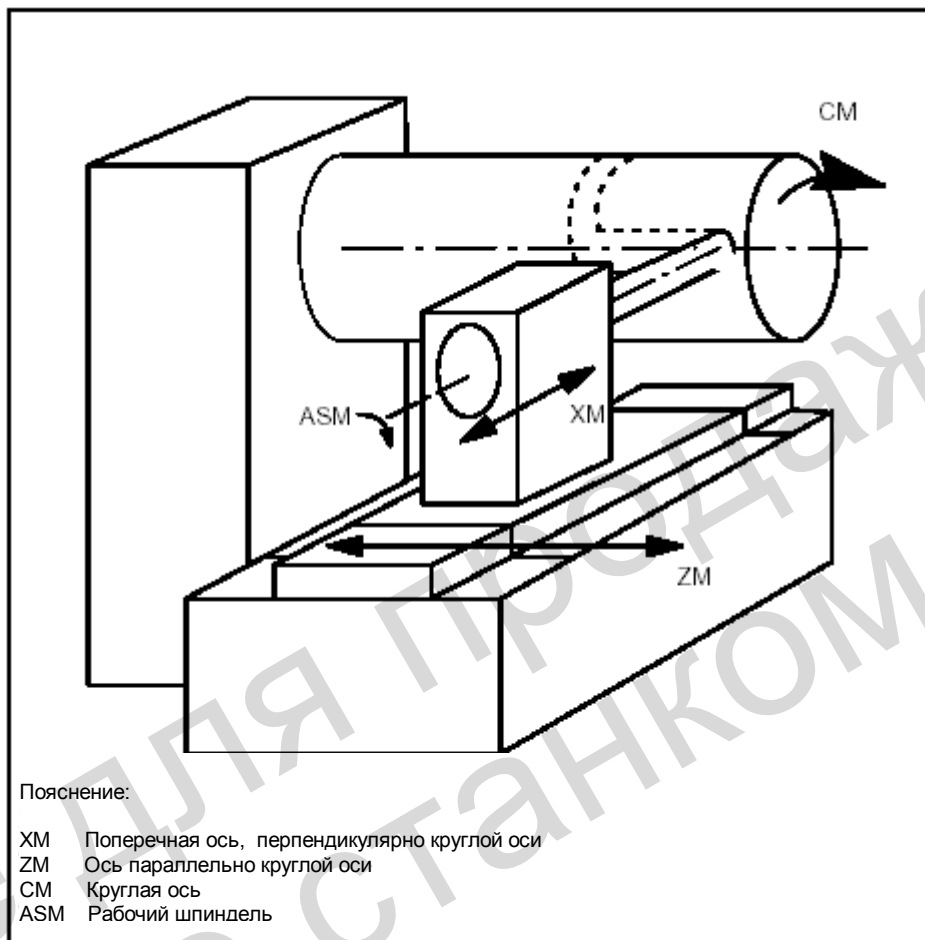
Обработка паза на боковой поверхности цилиндра с помощью кинематики X-C-Z
